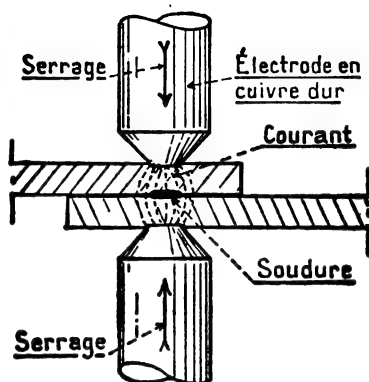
Soudure par points : les deux tôles à assembler sont fortement serrées entre deux électrodes en cuivre et on y fait passer pendant une durée de 0,01 à 0,3 seconde un courant de 5 000 à 50 000 ampères sous une tension de 2 à 10 volts.
